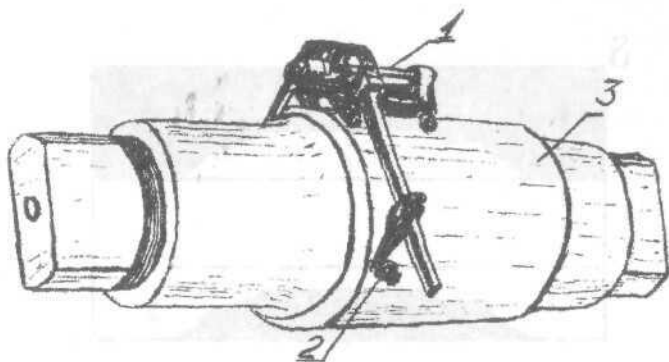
Пасометр: 1 – візок; 2 – індикатор; 3 – бочка валка
